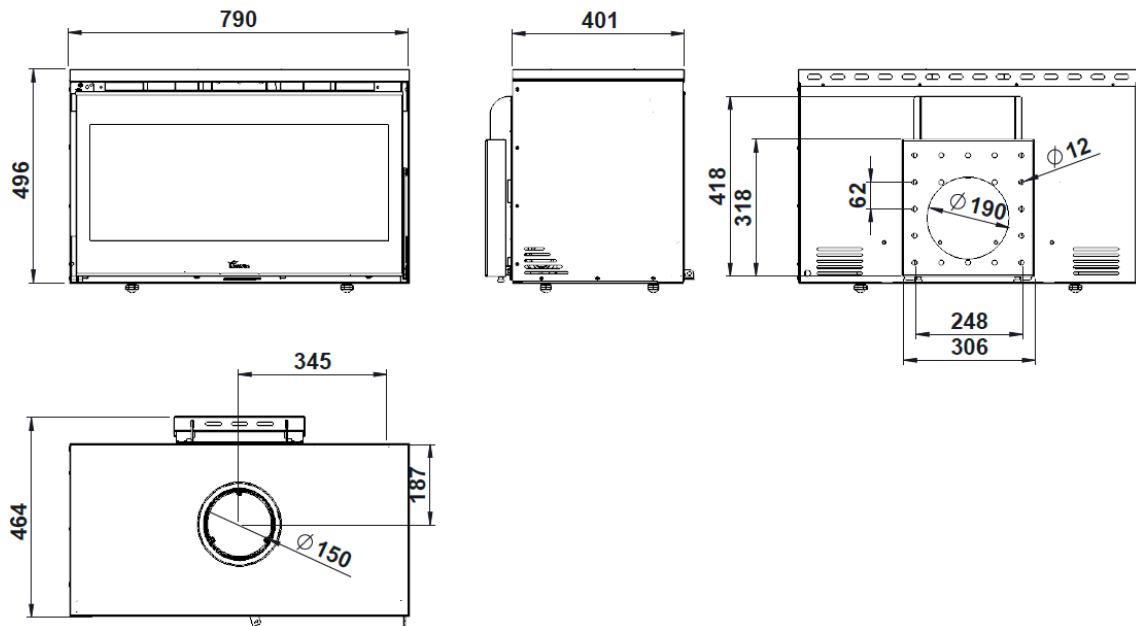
Dimensões em mm do aparelho PARIS 800 MURAL
